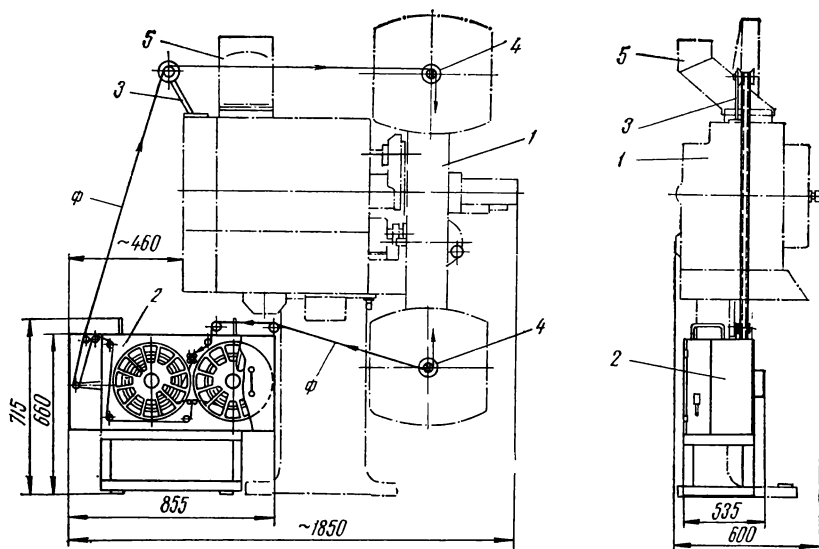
Габаритные размеры и схема расположения кинопроектора 23КПК и магазина-приставки БМП-35
